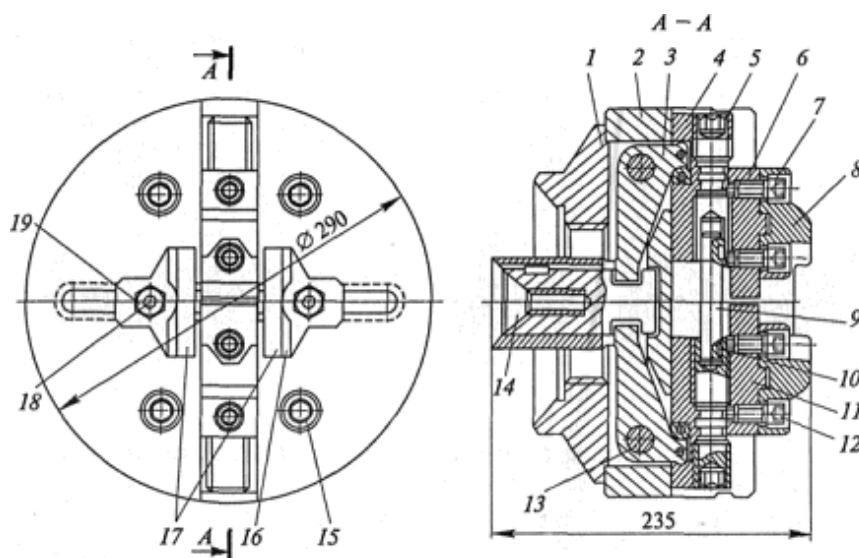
Автоматизований двокулачковий патрон:
